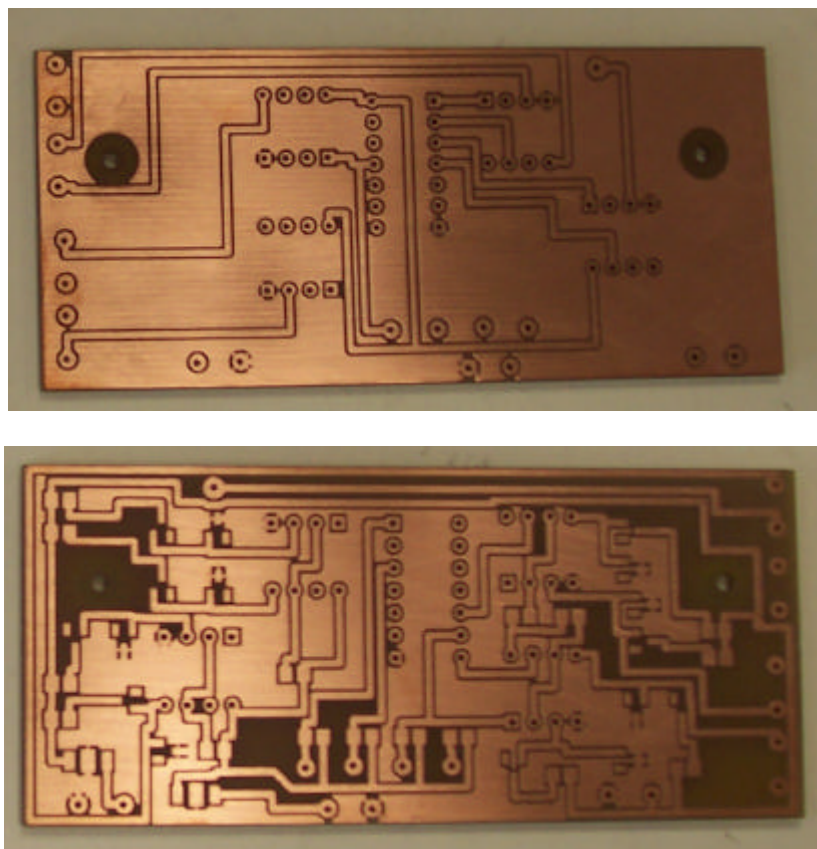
Caras frontal y trasera de la placa de circuito impreso para el control del atenuador programable, fabricada con la fresadora LPKF del CAY
